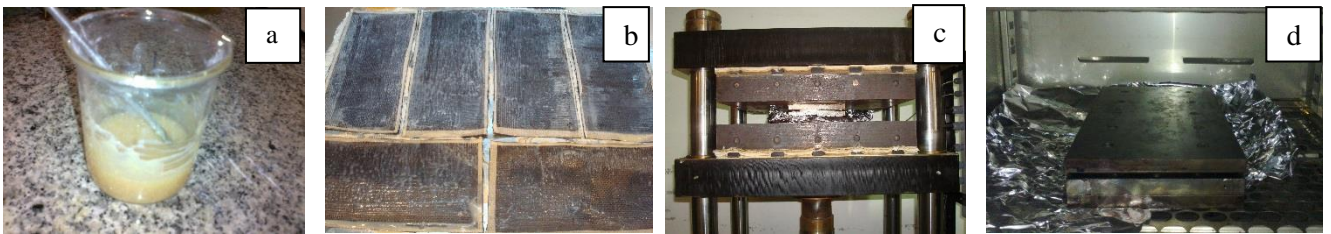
Procesamiento del material compuesto con resina modificada con partículas: a) Mezcla, b) Fibras impregnadas, c) Molde en prensa hidráulica, d) Molde en la estufa.
